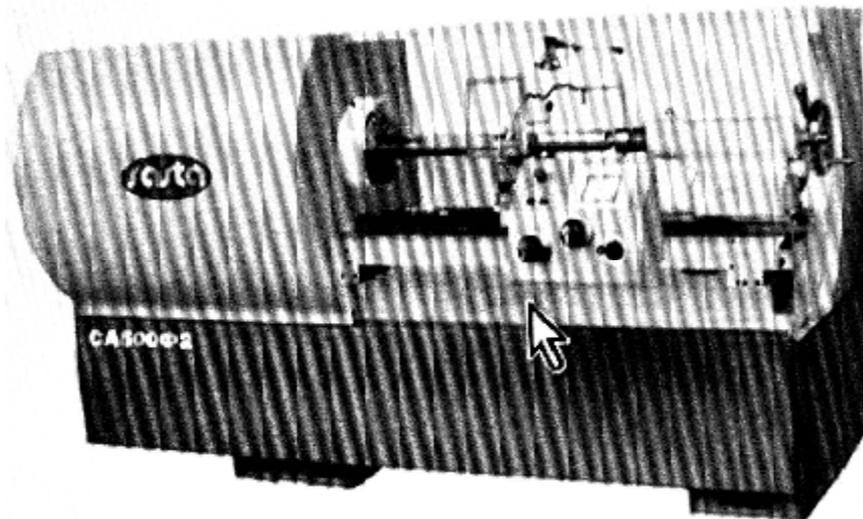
Универсальный токарный станок СА 500Ф2 с оперативной системой управления
